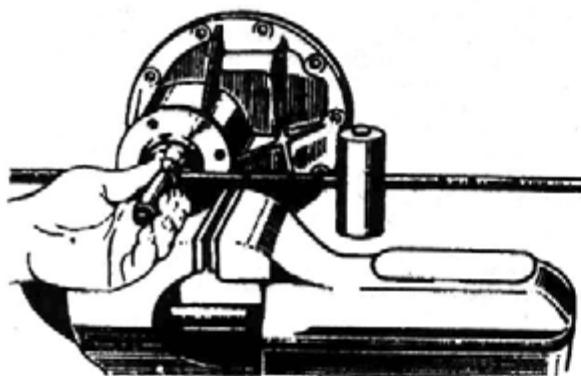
Проверка предварительного натяга подшипников ведущей шестерни
